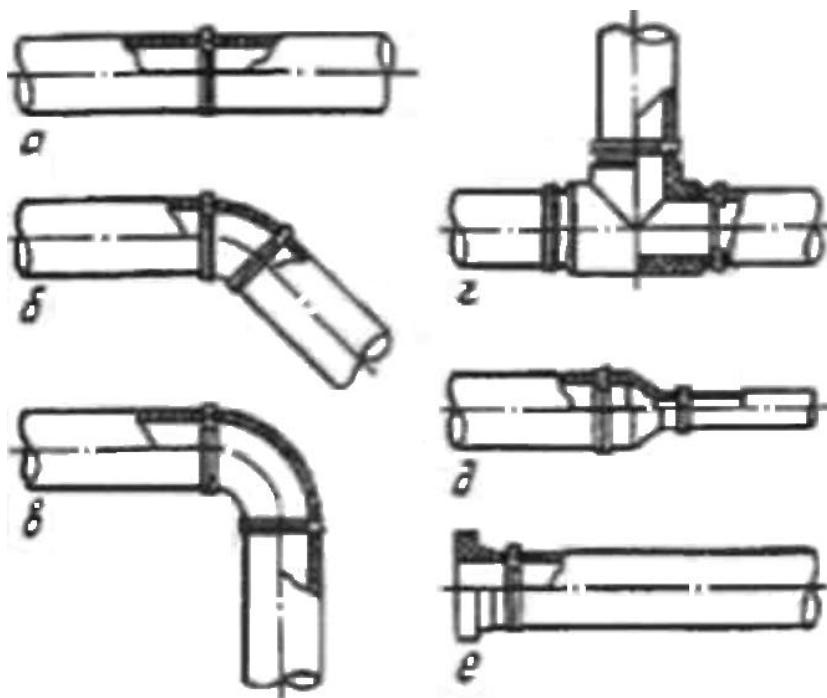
Сварные стыковые соединения труб и соединительных деталей из ПНД: *а* – труба с трубой; *б, в* – труб с угольниками соответственно 45° и 90°; *г* – труб с тройником; *д* – труб с переходом; *е* – трубы с втулкой под фланец
